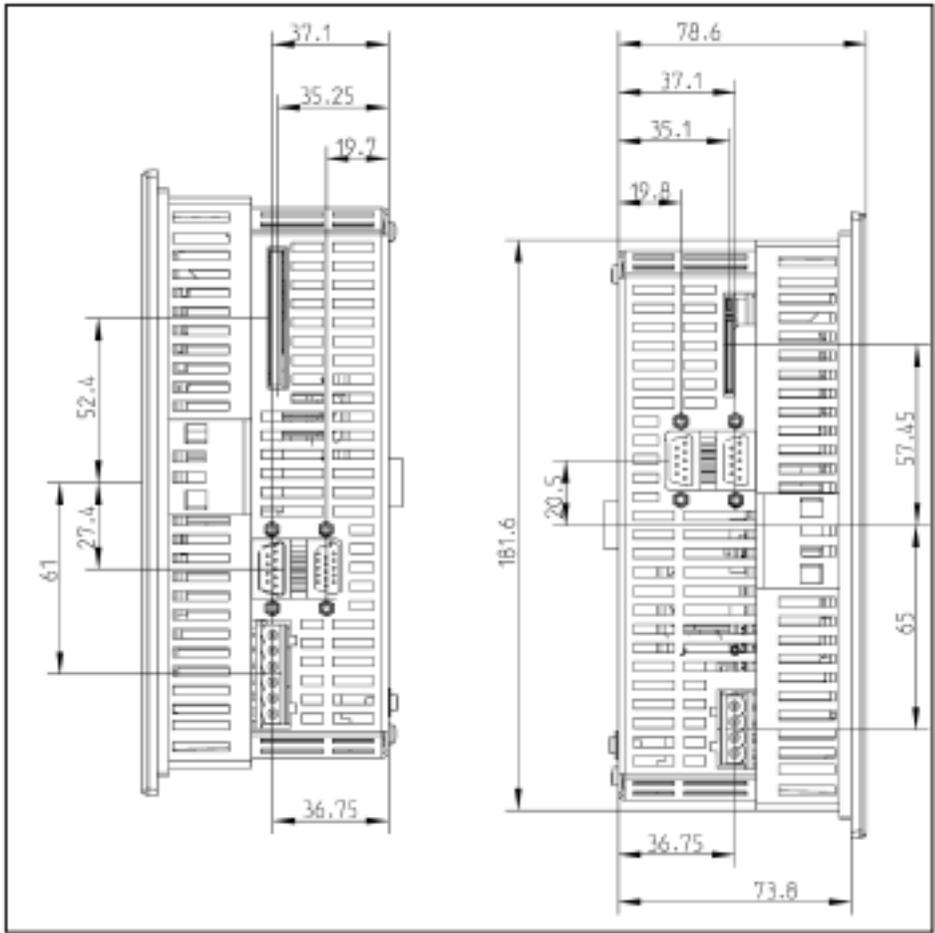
C7-635 Touch 的尺寸图(单位 mm)
